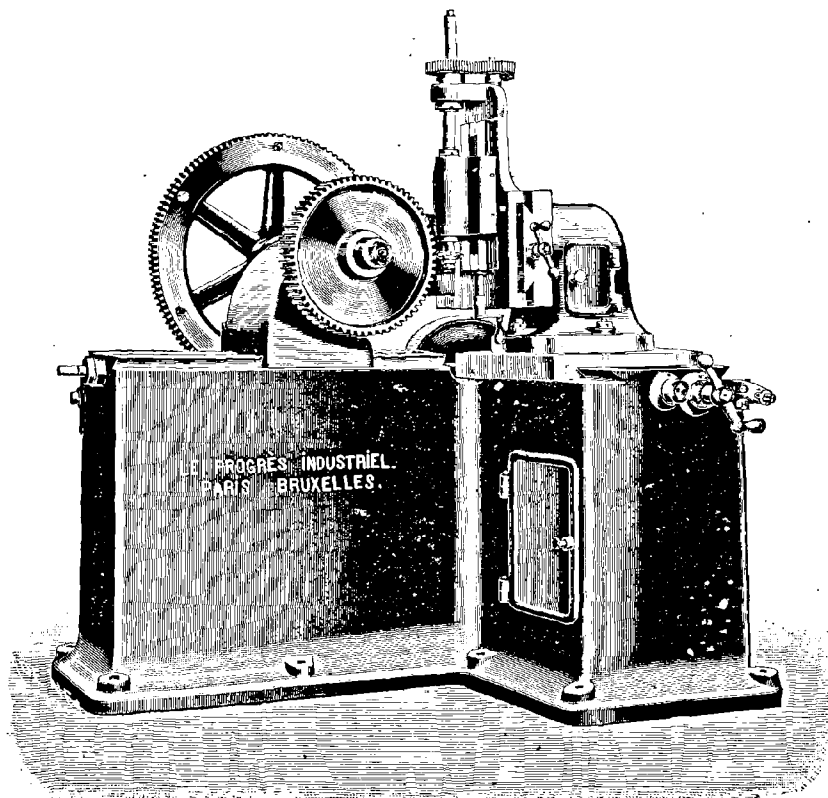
Machine à tailler les engrenages du Progrès Industriel.
